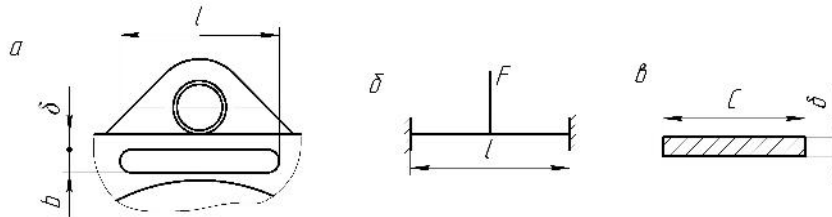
Схеми пружної ділянки: а - конструктивна; б – розрахункова; в – поперечний переріз пружної ділянки
